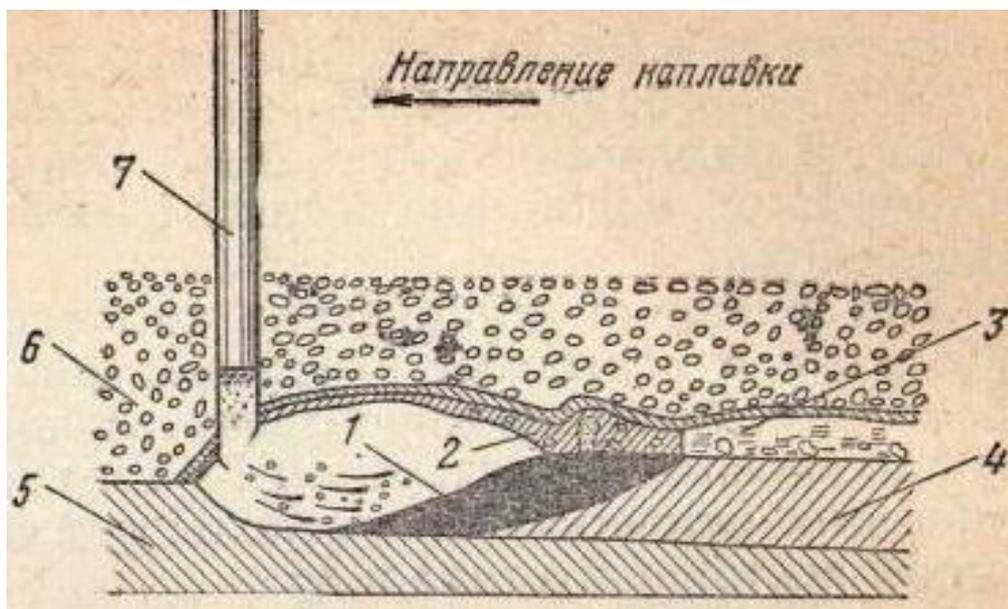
Схема сварочной ванны при наплавке под флюсом: 1 – жидкий металл; 2 – жидкий шлак; 3 – шлаковая корка; 4 – наплавленный металл; 5 – основной металл (детали); 6 – слой флюса; 7 – электродная проволока
